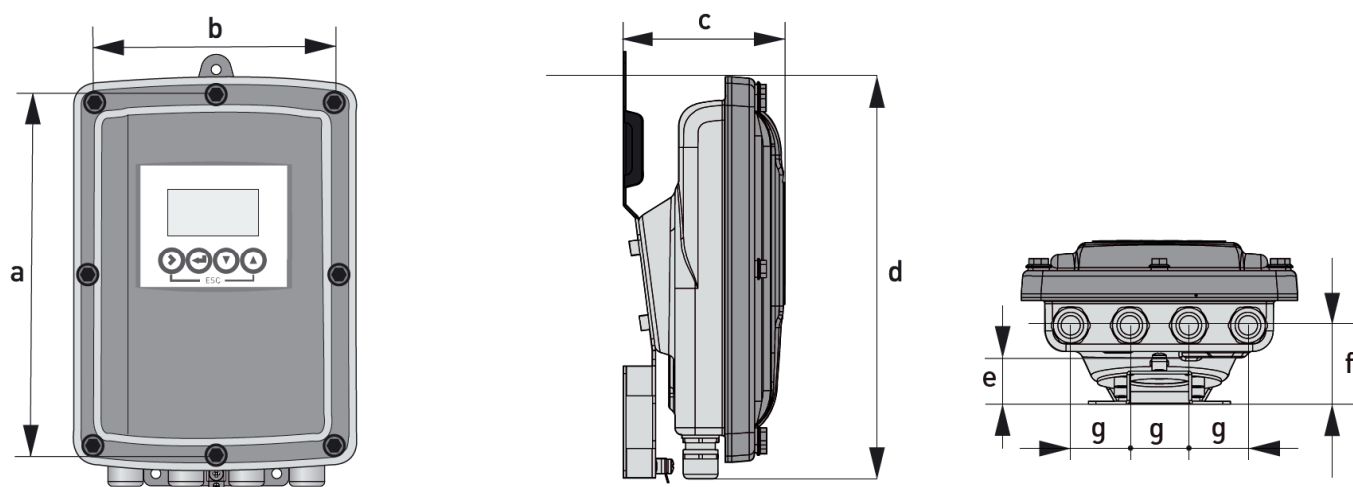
Габаритные размеры раздельного исполнения (для настенного монтажа) и компактного исполнения * с корпусом из нержавеющей стали
